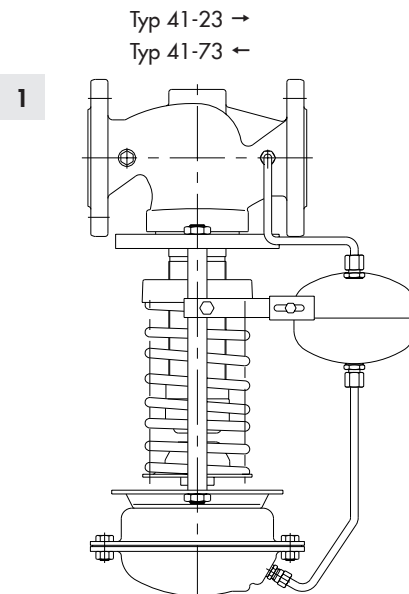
Steuerleitungsbausatz mit Ausgleichsgefäß für Dampf
